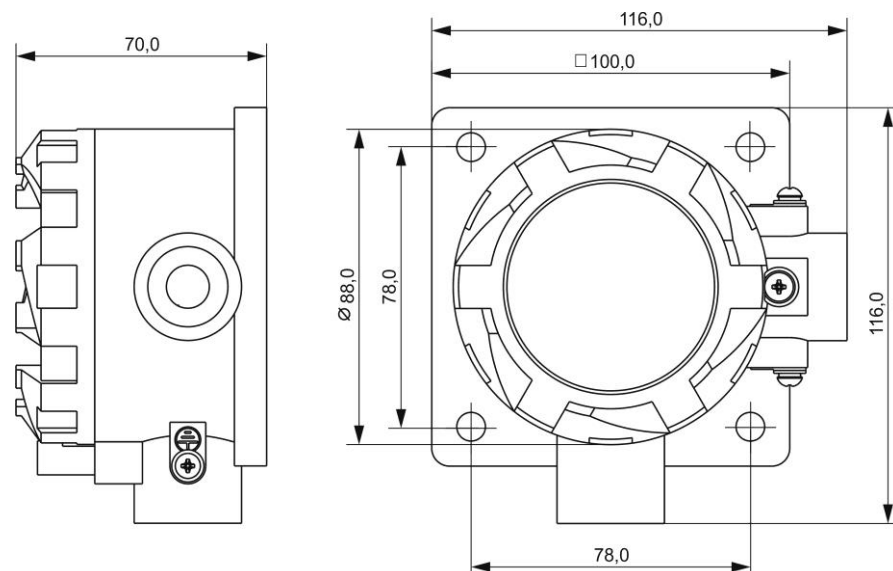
Габаритные размеры ИП 0304/М3-Н-ВР12-И
